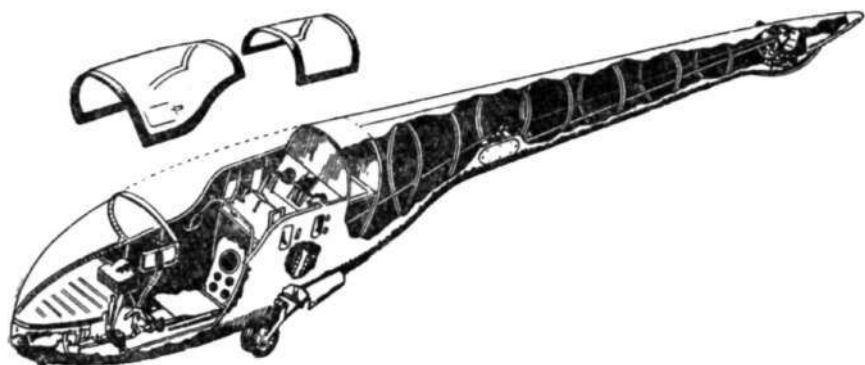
Конструкция фюзеляжа планера А-13. Фюзеляж не имеет стрингеров. Нагрузки воспринимаются толстой, подкрепленной шпангоутами и обшивкой.
